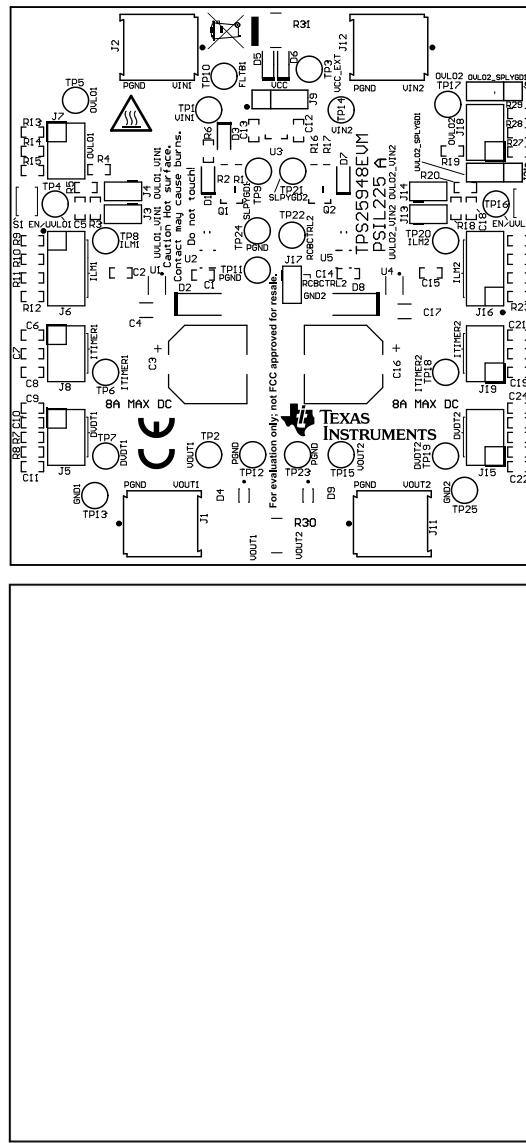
TPS25948EVM 电路板 (a) 顶层装配图 (b) 底层装配图
